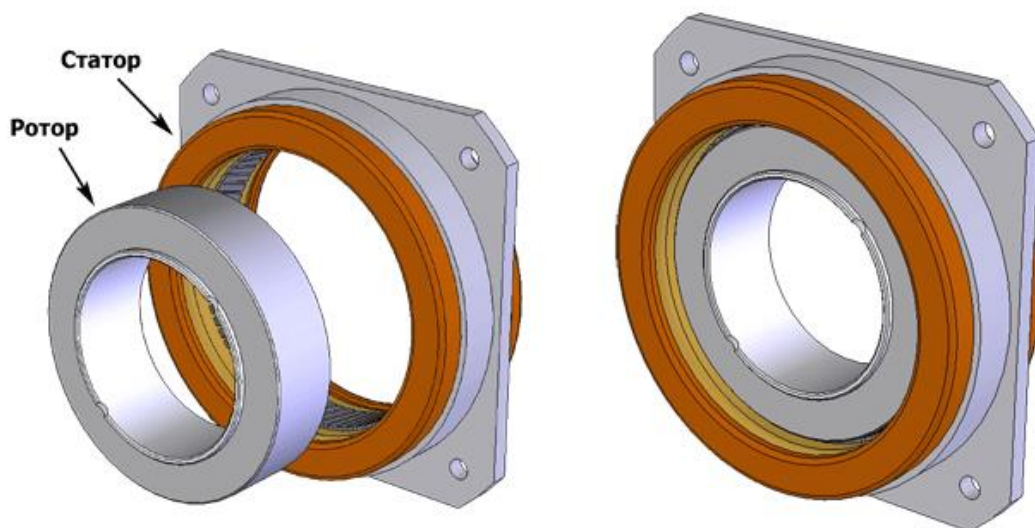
Двигатель ДБМ (Двигатель Бесконтактный Моментный)
